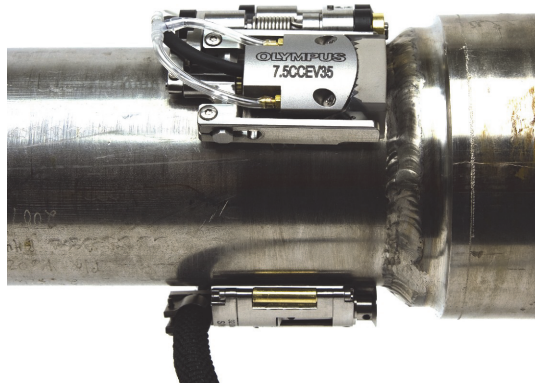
Inspección del acoplamiento de tubería a componente con la configuración del escáner de un sólo lado
